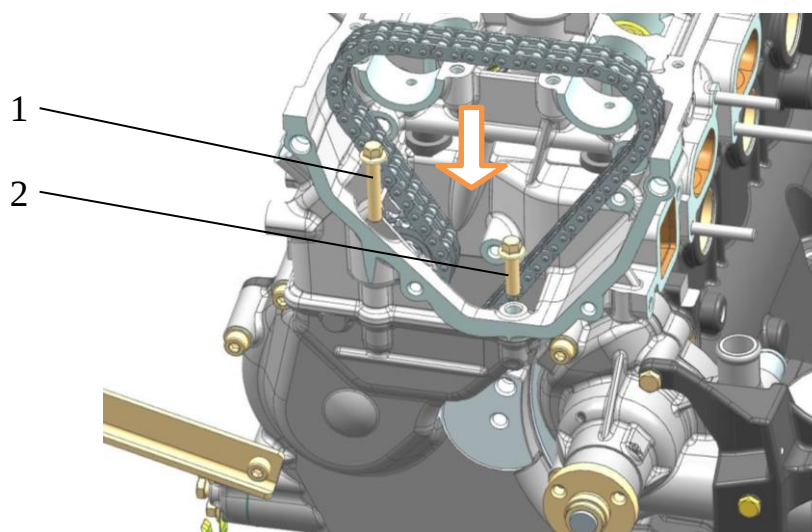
Затяжка болтов крепления крышки цепи к головке цилиндров
